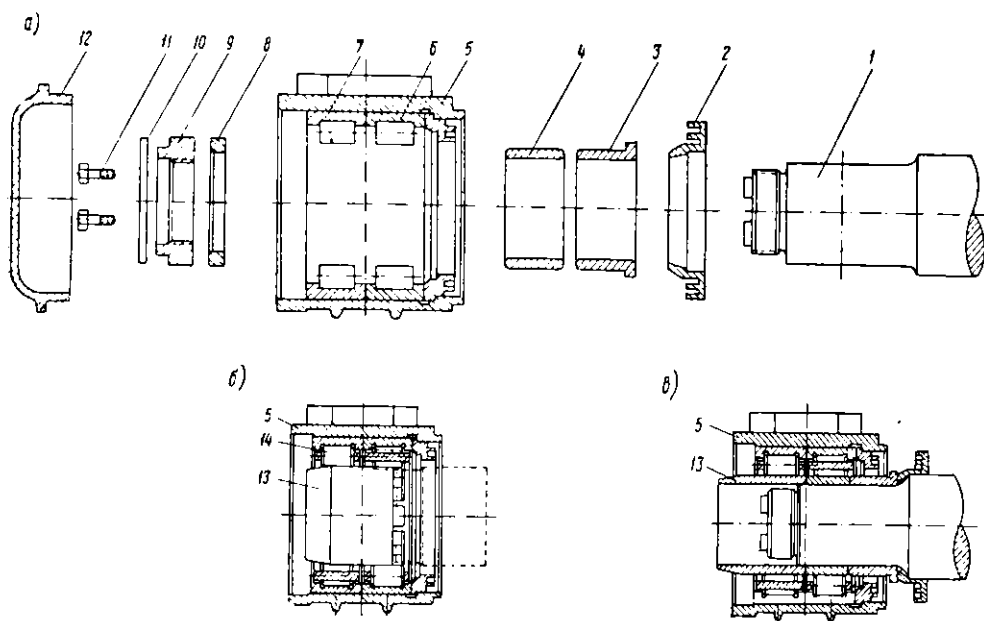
Порядок монтажа буксы с цилиндрическими роликовыми подшипниками на горячей посадке
